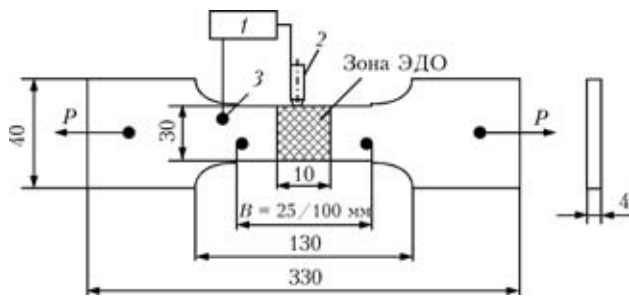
Схема ЭДО образцов основного металла и сварного соединения сплава АМг6 для испытаний на одноосное растяжение: 1 — установка для ЭДО; 2 — электрод; 3 — крепление обратного провода;  $P$  — растягивающее усилие
